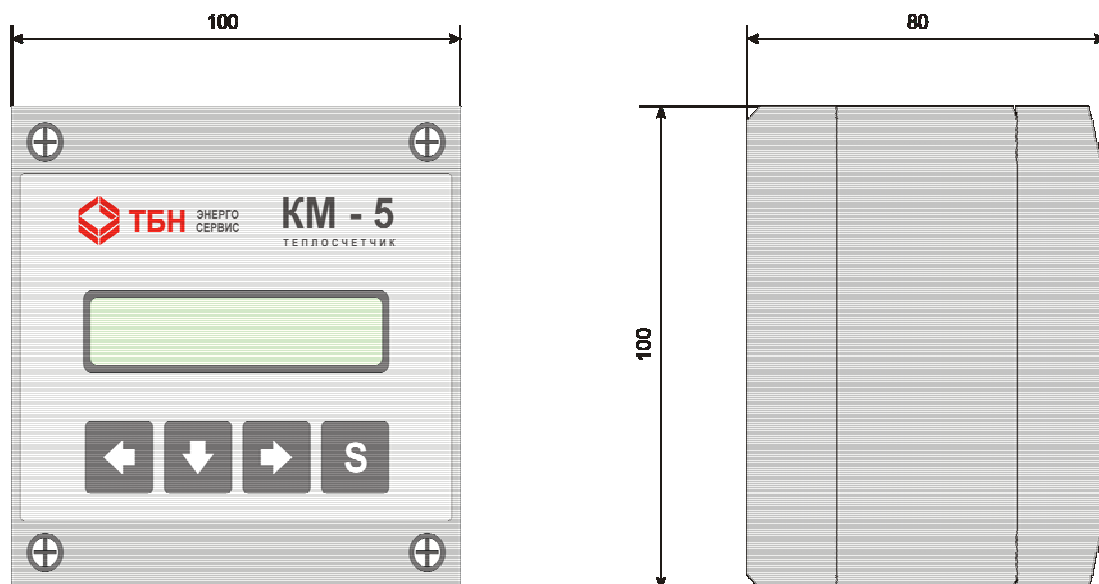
Внешний вид, габаритные и установочные размеры электронного блока КМ-5.
